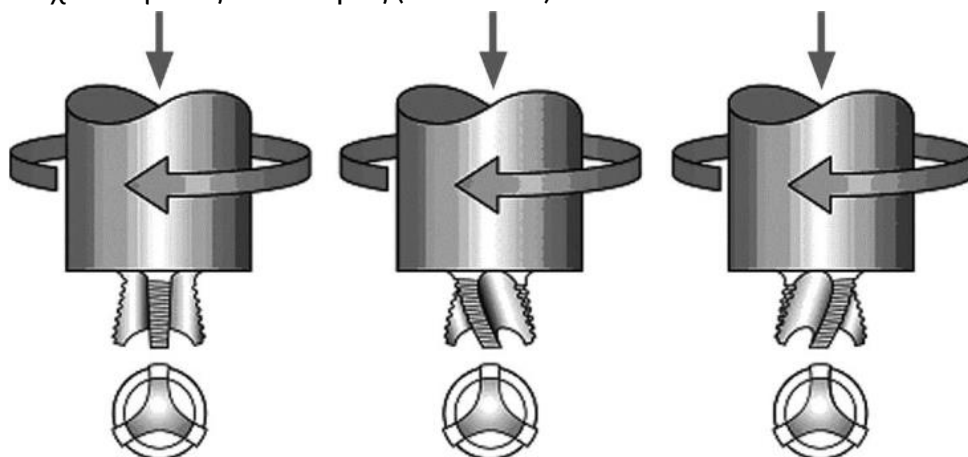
Εργαλεία που αναπτύχθηκαν από το The Welding Institute (4)
